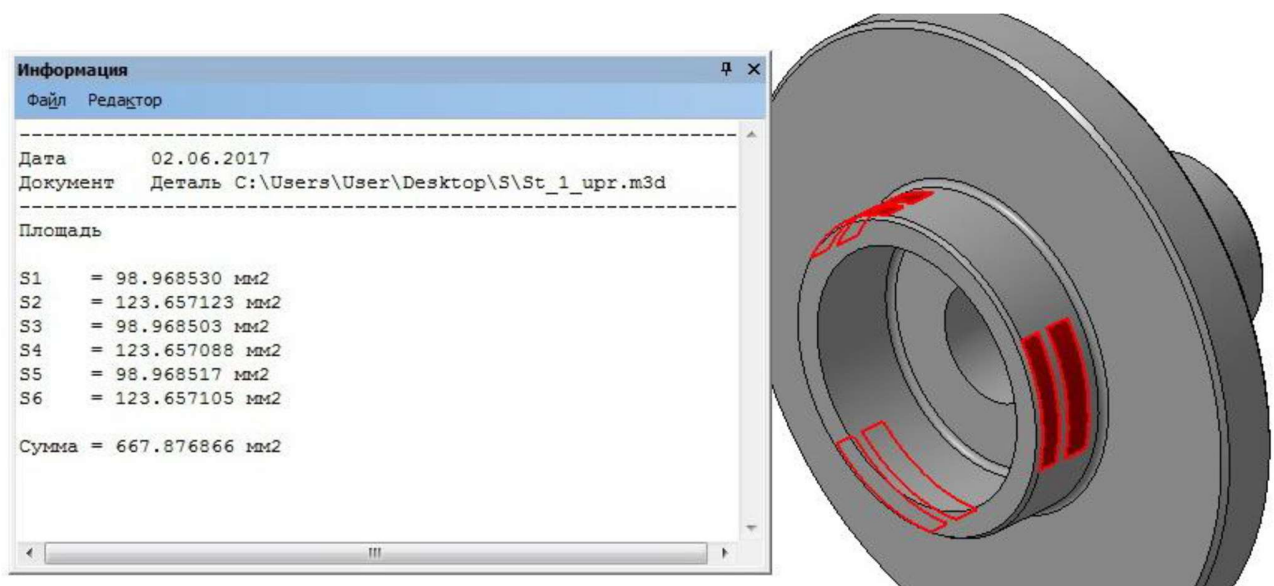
Розрахунок площі закріплення заготовки
